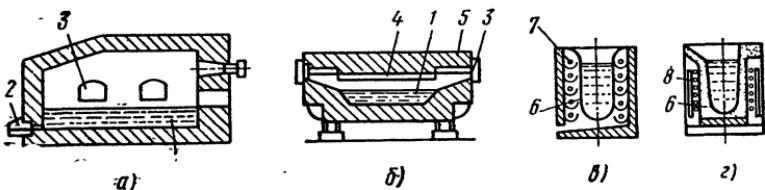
Схемы печей для плавки алюминиевых сплавов:
